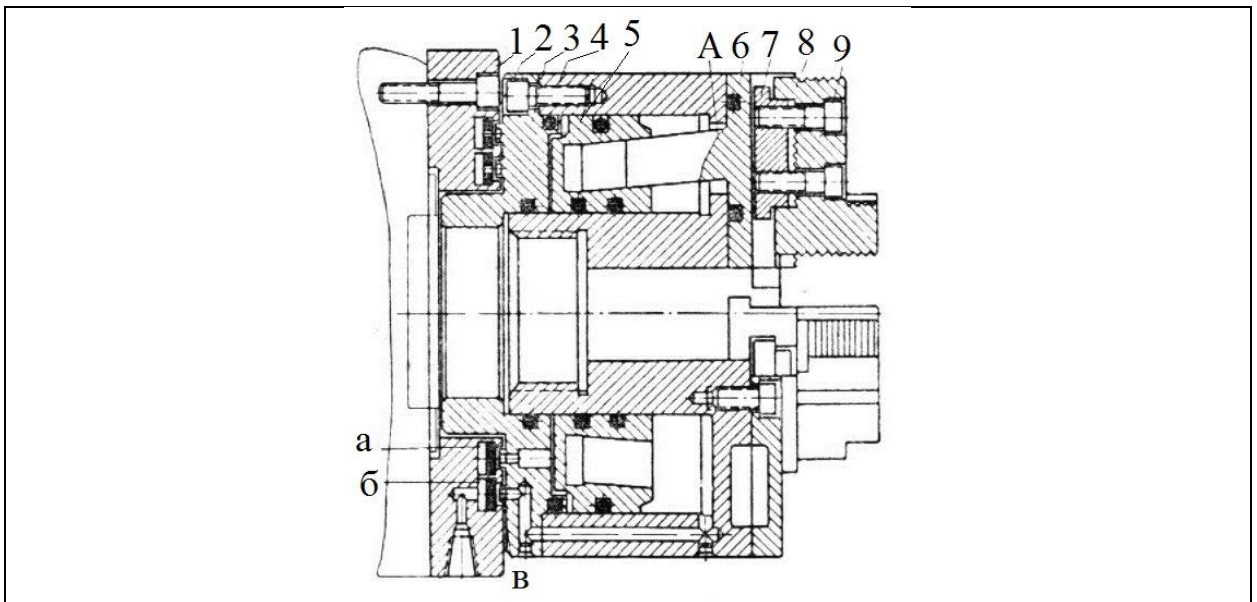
Трикулачковий самоцентрувальний патрон з пневматичним приводом 1-повітророзподільне кільце; 2-гумова шайба; 3-накривка; 4-корпус; 5-поршень; 6-повзун; 7-підкладка; 8-закріпний кулачок; 9-гвинт
